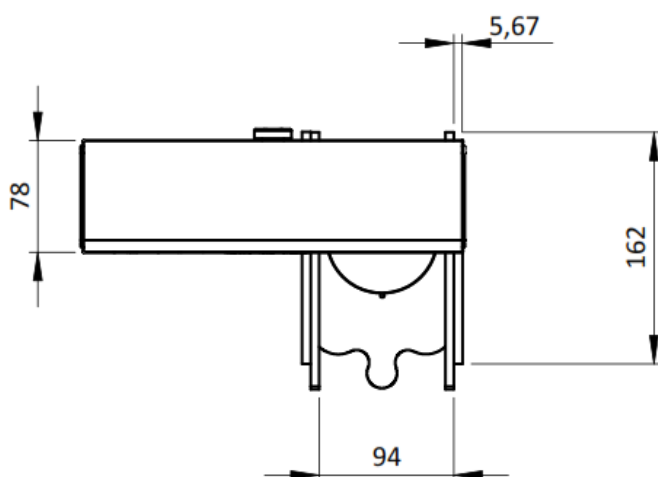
Esquema superior dimensional del sistema óptico de la impresora.
